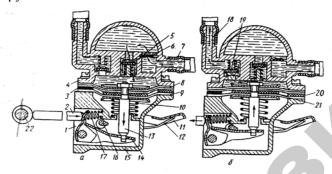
Схема работы топливного насоса двигателя ВАЗ:
